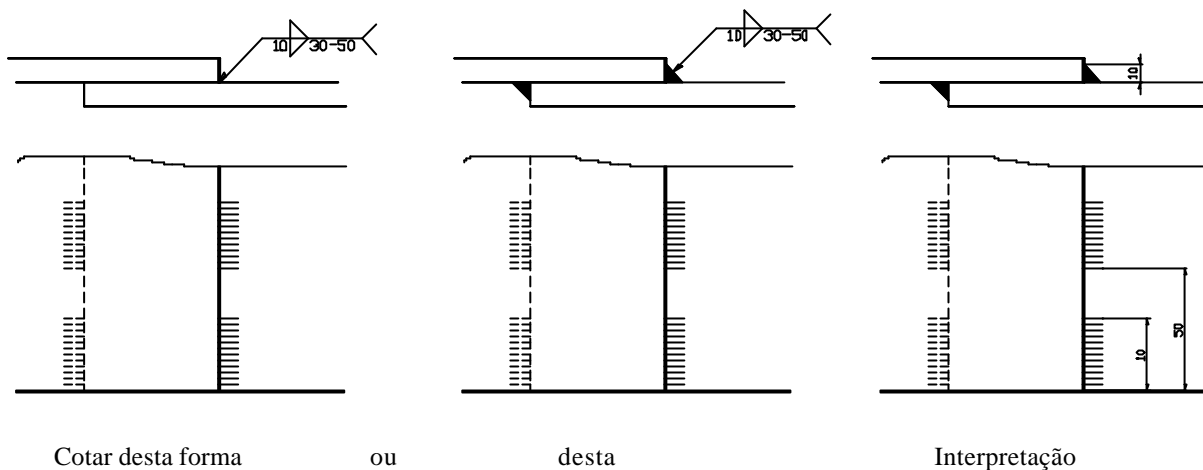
Cotagem com comprimento e passo do cordão de solda
